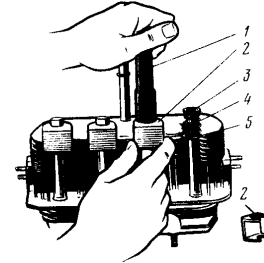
Сжатие пружин с шайбами оправкой и крепление их скобами: 1 — оправка; 2 — скоба; 3 и 5 — шайбы; 4 - пружина
